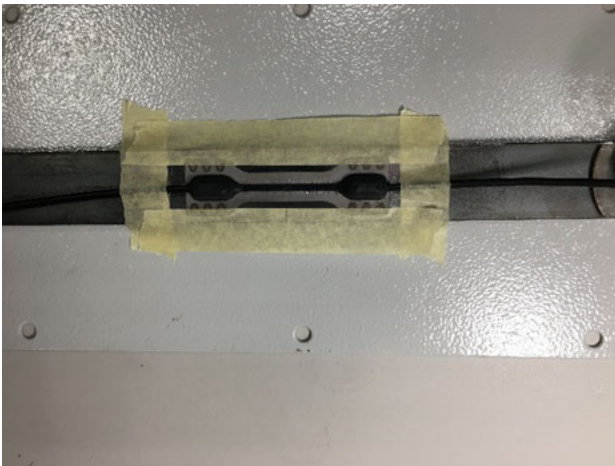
Vollständig angeschweißter Sensor
